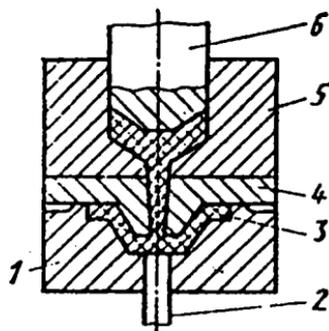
Схема пресс-формы литьевого прессования: 1 — матрица; 2 — выталкиватель; 3 — изделие; 4 — пуансон; 5 — загрузочная камера; 6 — пуансон загрузочной камеры
